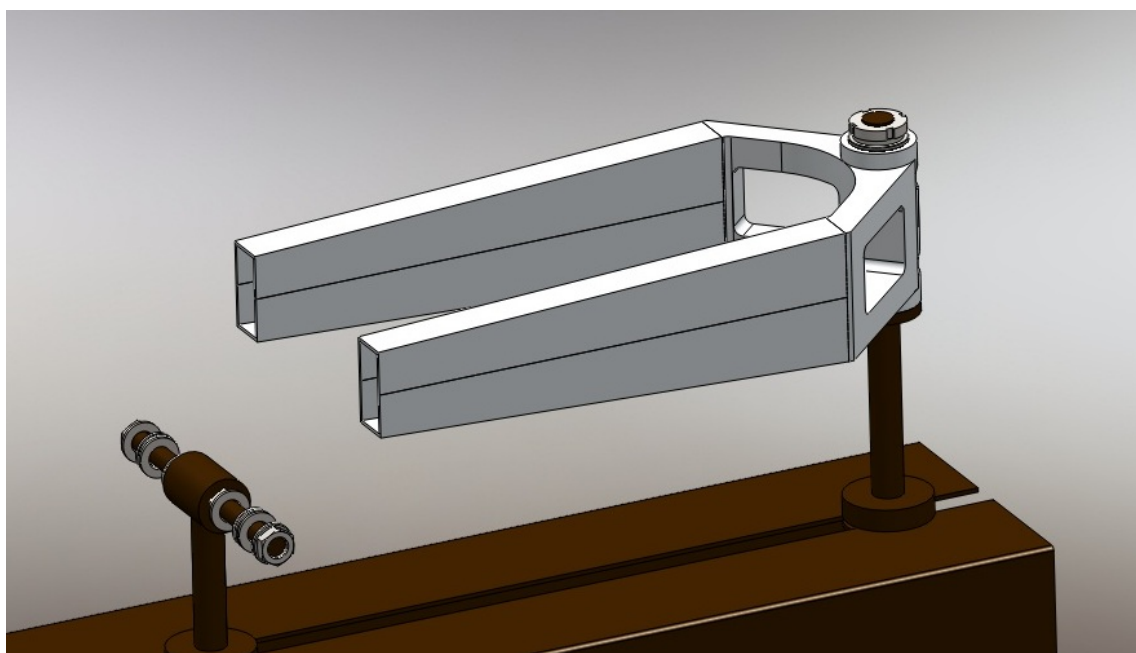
Soldadura de la pipa con las vigas
